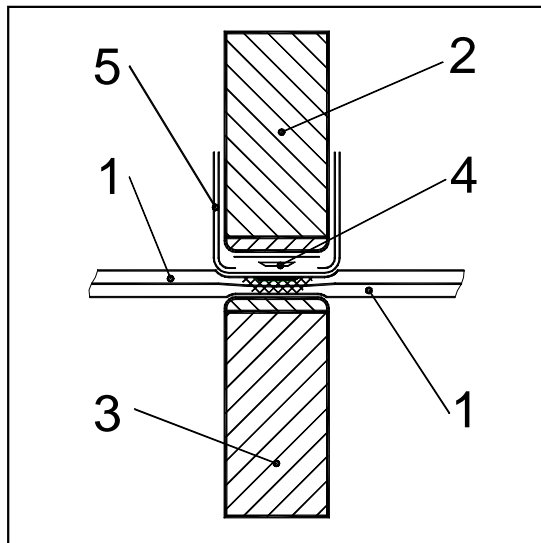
Skizze zum Wärme-Impuls-Schweißverfahren
